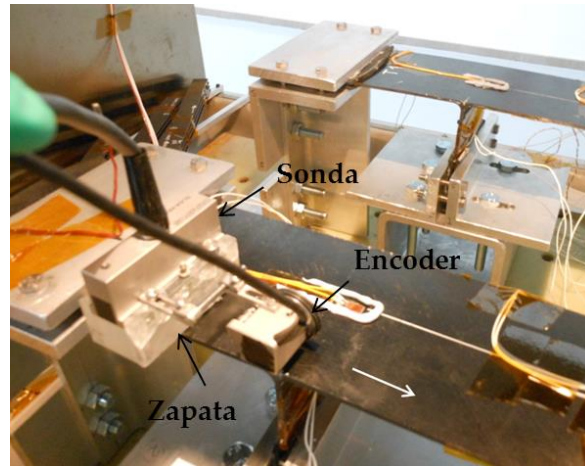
Montaje para la inspección UT-PA sobre especímenes en T.
